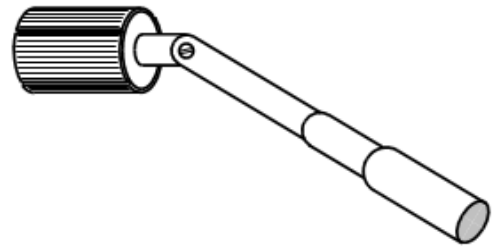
Двухкоординатный цилиндрический датчик на штанге. Конструктивное исполнение
